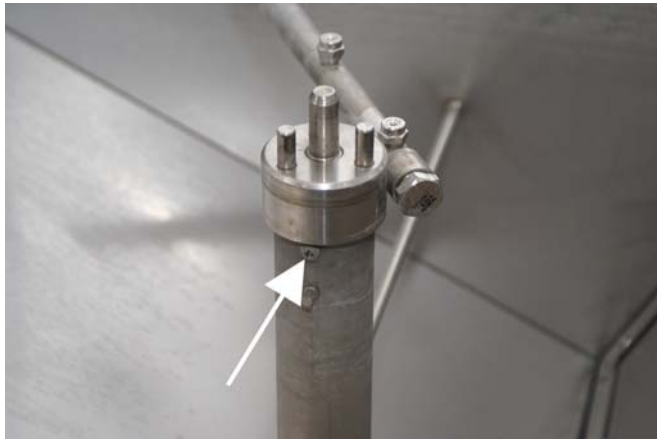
Halteschrauben für Lager, vordere Schraube
